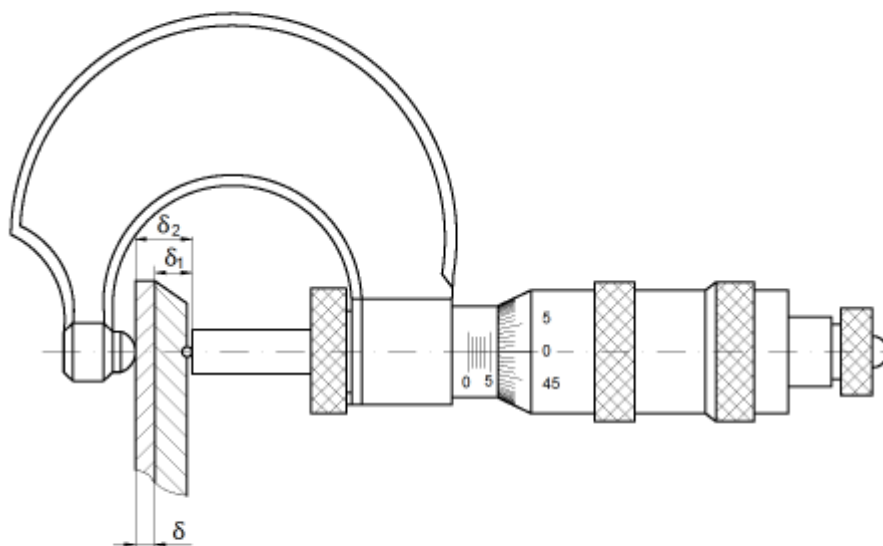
Схема вимірювання товщини наплавленого шару металу
